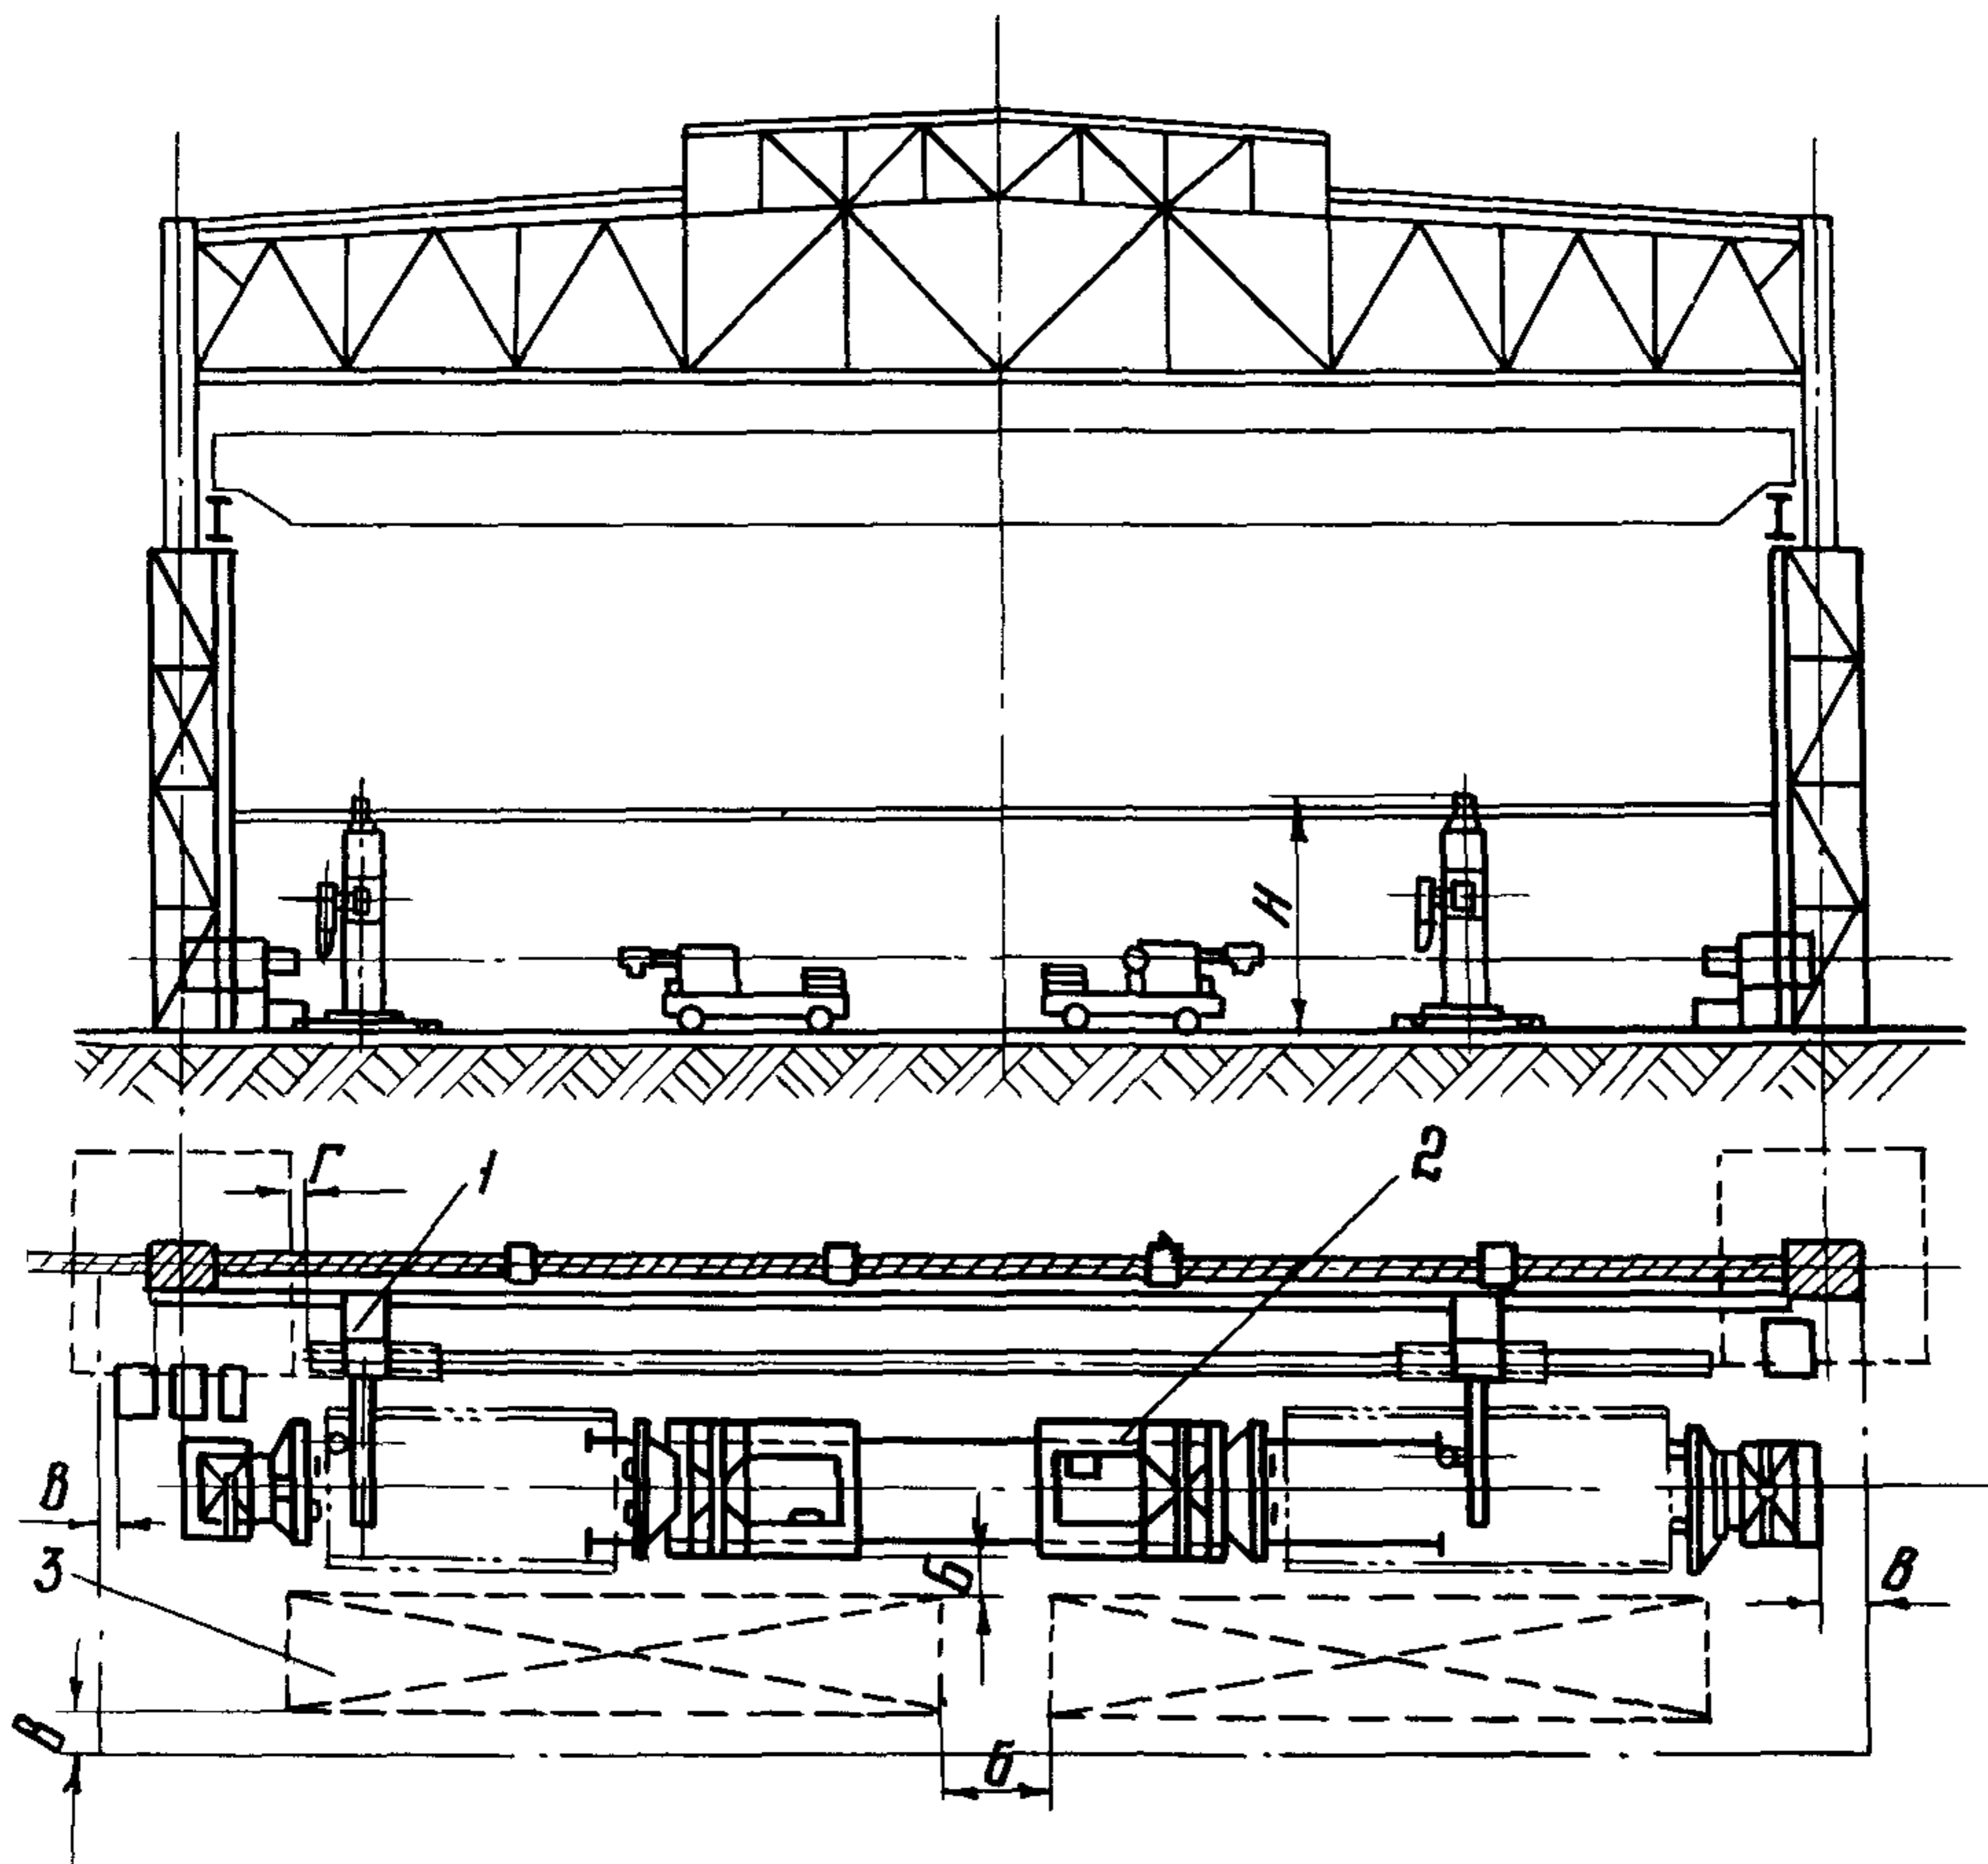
Г. Размещение участка автоматической сварки с велосипедной тележкой:
